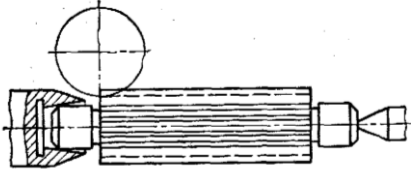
Схема наскрізного фрезерування шліців з використанням оправки зі зворотнім конусом
